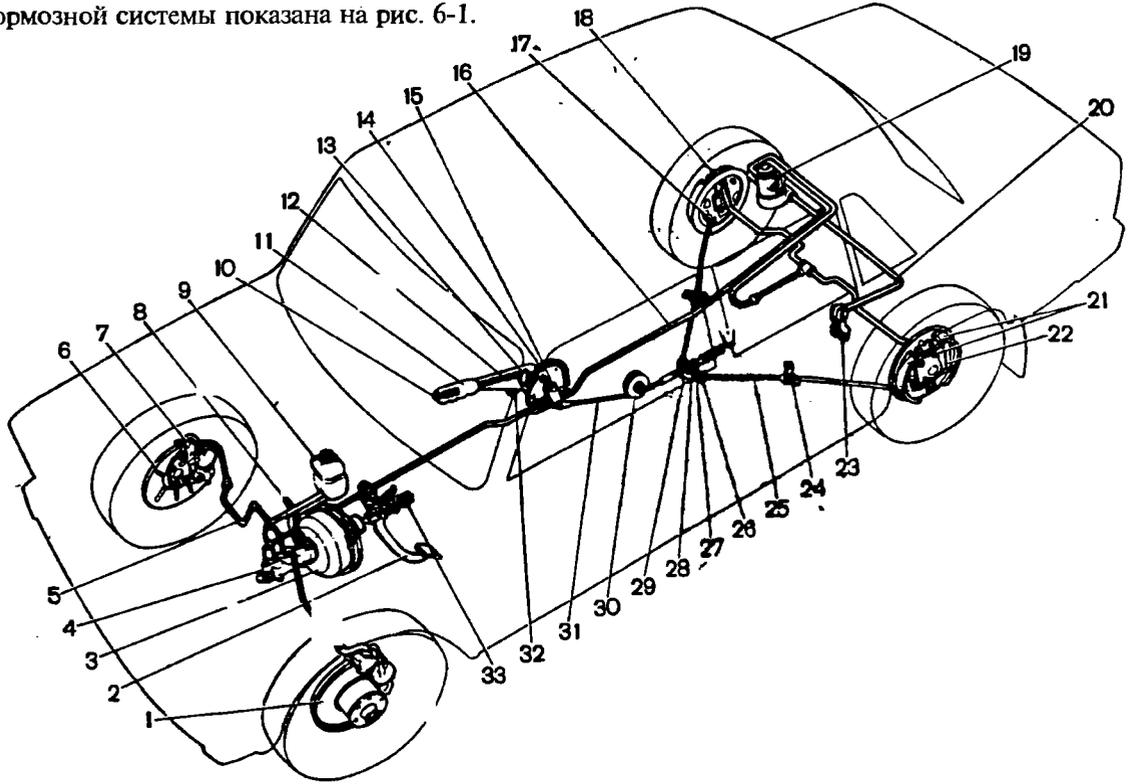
Схема тормозной системы: 1 - диск тормоза; 2 - педаль тормоза; 3 - вакуумный усилитель; 4 - главный цилиндр гидропривода тормозов; 5 - трубопровод контура привода передних тормозов; 6 - защитный кожух переднего тормоза; 7 - суппорт переднего тормоза; 8 - вакуумный трубопровод; 9 - бачок главного цилиндра; 10 - кнопка рычага привода стояночного тормоза; 11 - рычаг привода стояночного тормоза; 12 - тяга защелки рычага; 13 - защелка рычага; 14 - кронштейн рычага привода стояночного тормоза; 15 - возвратный рычаг; 16 - трубопровод контура привода задних тормозов; 17 - фланец заднего наконечника оболочки троса; 18 - колесный цилиндр заднего тормоза; 19 - регулятор давления задних тормозов; 20 - рычаг привода давления; 21 - колодки тормоза; 22 - рычаг ручного привода колодок; 23 - тяга рычага привода регулятора давления; 24 - кронштейн крепления переднего наконечника оболочки троса; 25 - задний трос; 26 - контргайка; 27 - регулировочная гайка; 28 - втулка; 29 - направляющая заднего троса; 30 - направляющий ролик; 31 - передний трос; 32 - упор включателя контрольной лампы стояночного тормоза; 33 - выключатель стоп-сигнала
